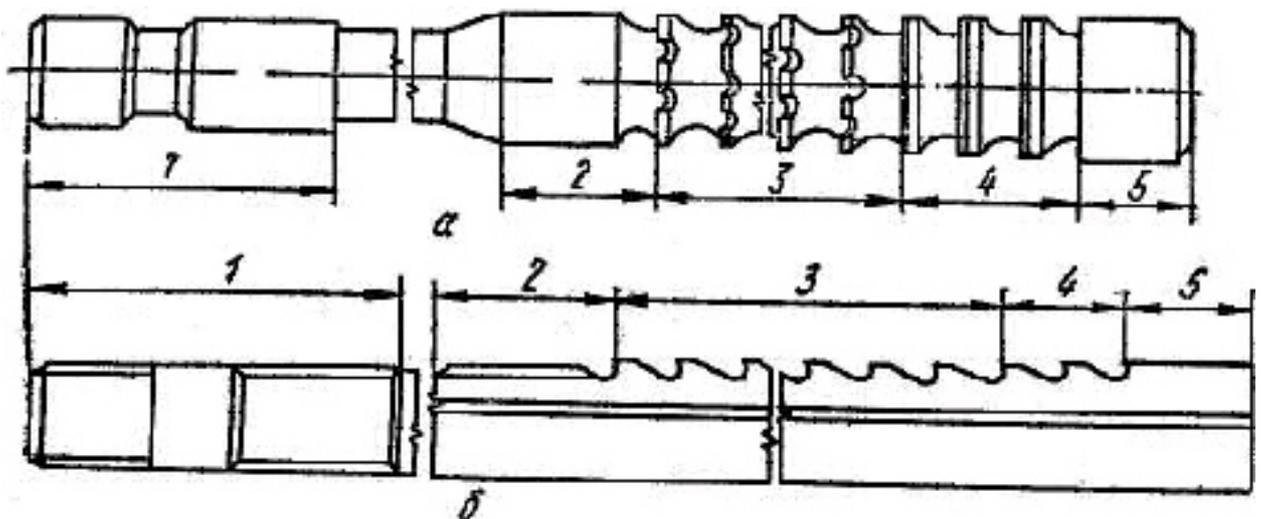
Конструкция цилиндрической (а) и шпоночной (б) протяжек
